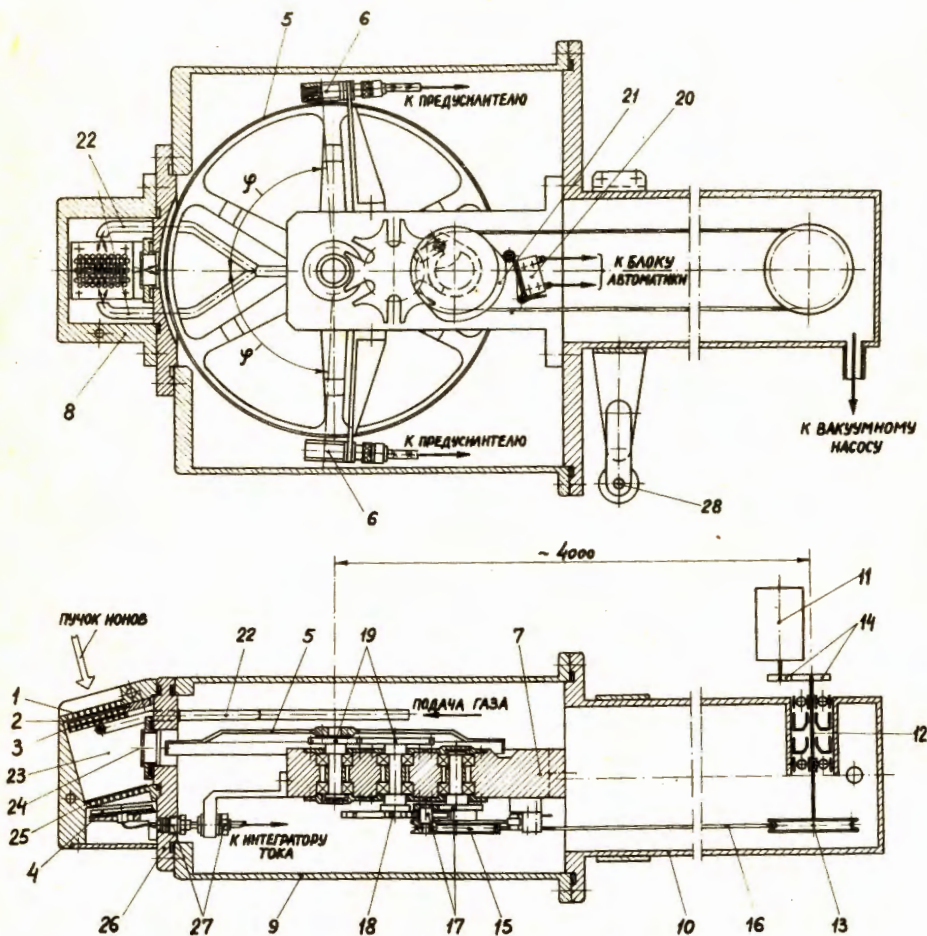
Конструкция головки пробника №3. 1 - входная решетка, 2 - входная фольга, 3 - мишень, 4 - коллектор тока, 5 - носитель-диск, 6 - детекторы, 7 - кронштейн, 8 - малый кожух головки, 9 - большой кожух, 10 - соединительная труба, 11 - двигатель, 12 - валик, проходящий через уплотнение, 13 - ведущий шкив, 14 - шестерни, 15 - ведомый шкив, 16 - тросик, 17 - водило с пальцем, 18 - мальтийский крест, 19 - шестерни, 20 - конечный выключатель, 21 - кулачок, 22 - трубки для подачи газа, 23 - тормозной объем, 24 - отверстие для выхода струи газа, 25 - выходные фольга с решетка, 26 - переходной фланец, 27 - разъем коллектора тока, 28 - ролик для передачи веса головки пробника на направляющую в камере циклотрона.
